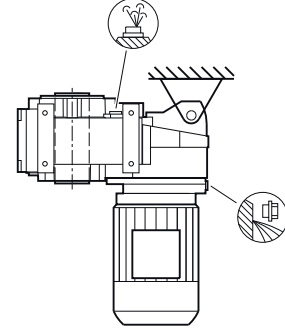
Düz dişli için montaj konumları DF/ZF Flanşlı model, Boyutlar 49 - 89 ve gövde flanşlı DZ/ZZ, Boyutlar 49 - 89
